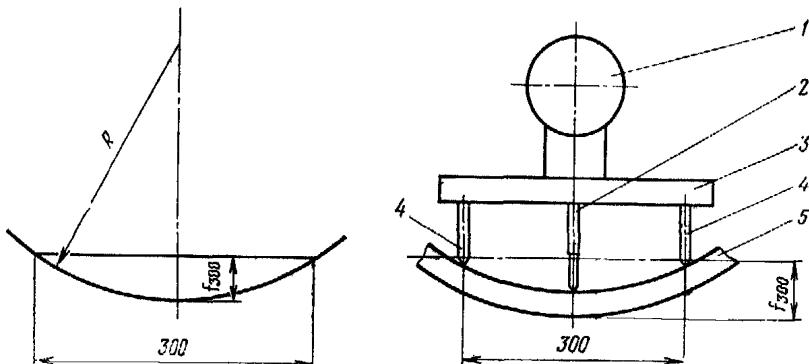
Схема прибора для измерения стрелки прогиба на базе 300 мм: 1 — индикатор; 2 — подвижная ножка прогибомера; 3 — планка; 4 — неподвижные опоры; 5 — наружная обшивка
